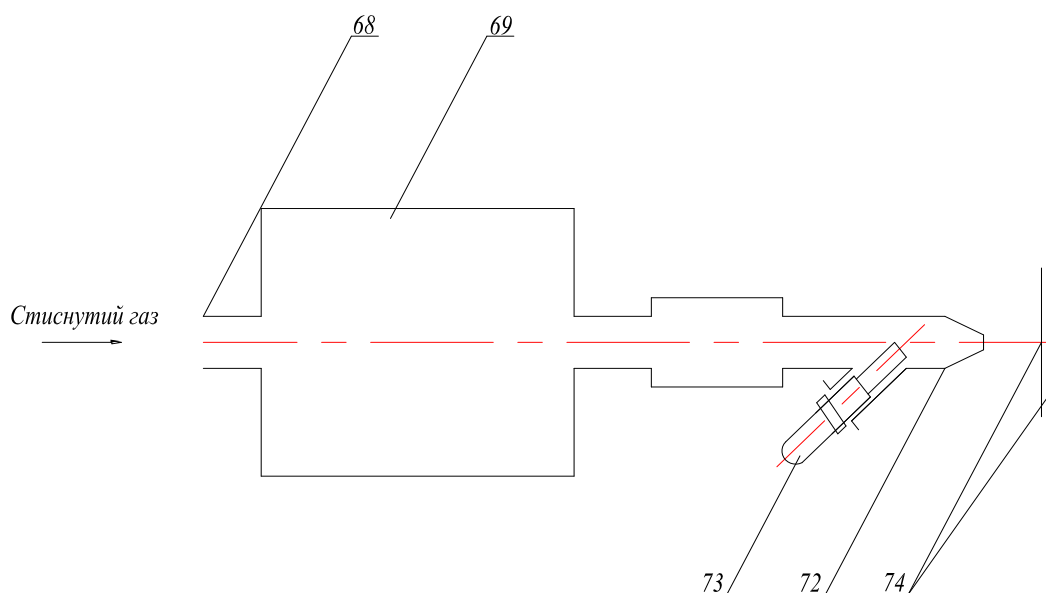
Пристрій для зварювання пакетів із термопластичних матеріалів газом-теплоносієм
